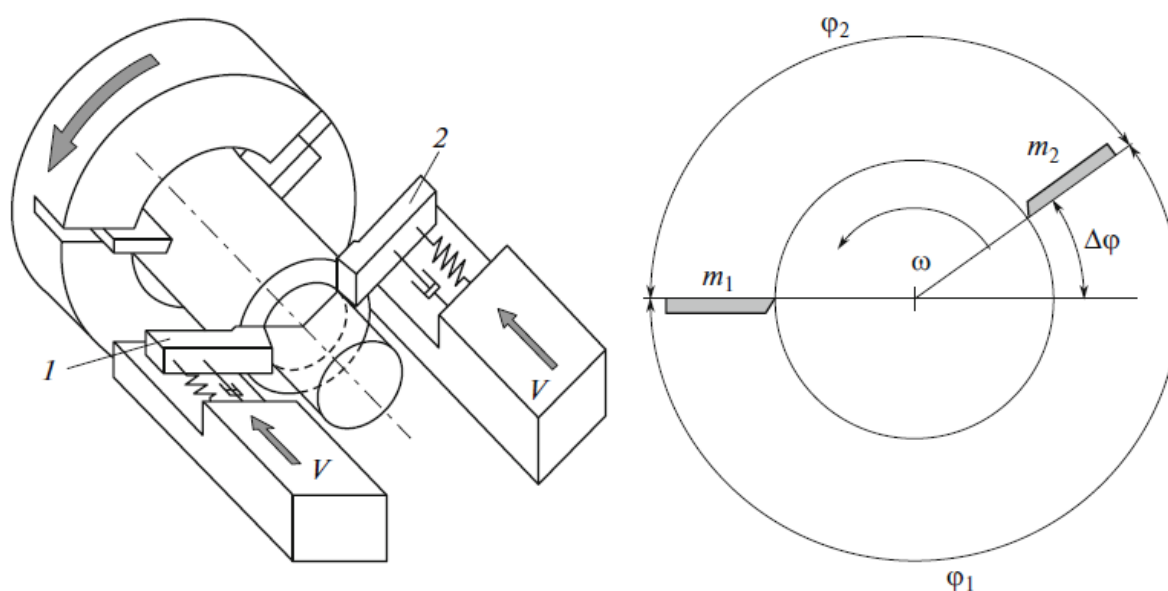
Схема обработки двух резцовой схемой: 1,2 - резцы
